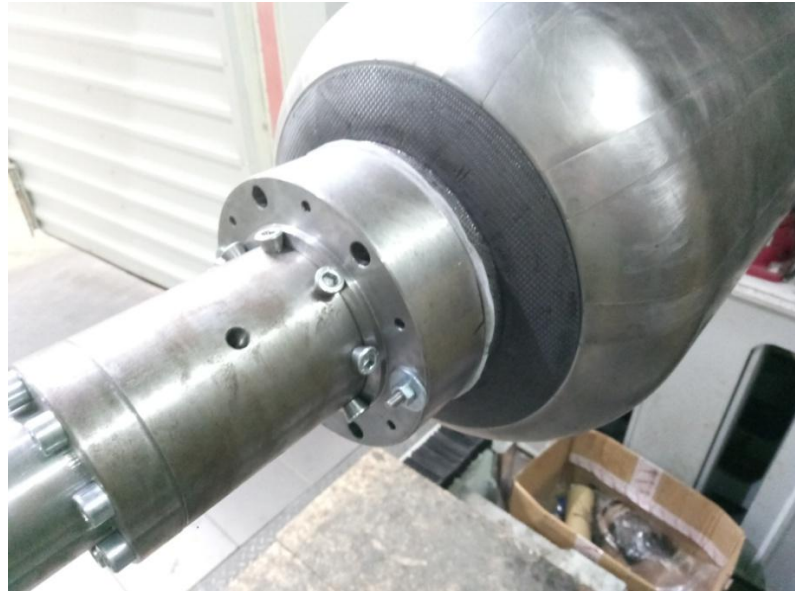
Оправка корпуса топливного бака с установленными фланцами
